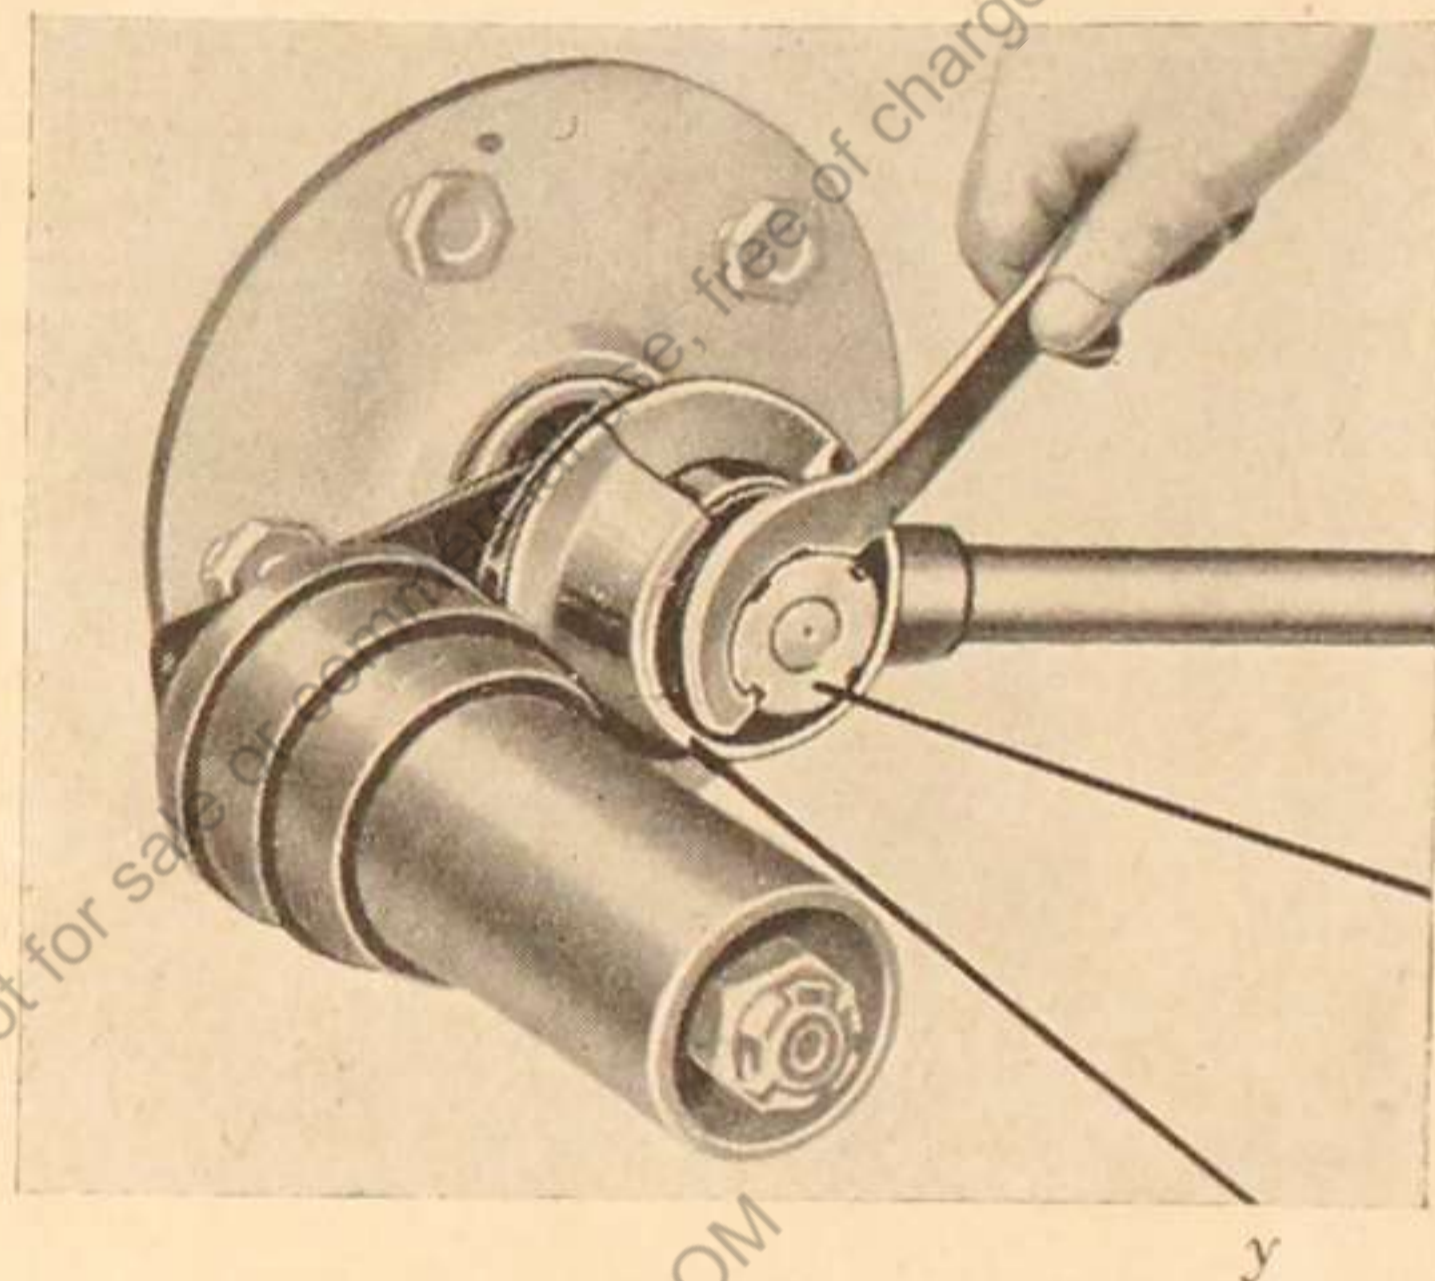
Einstellen der Stoßdämpfer. y Sprengring, z Ringmutter.
